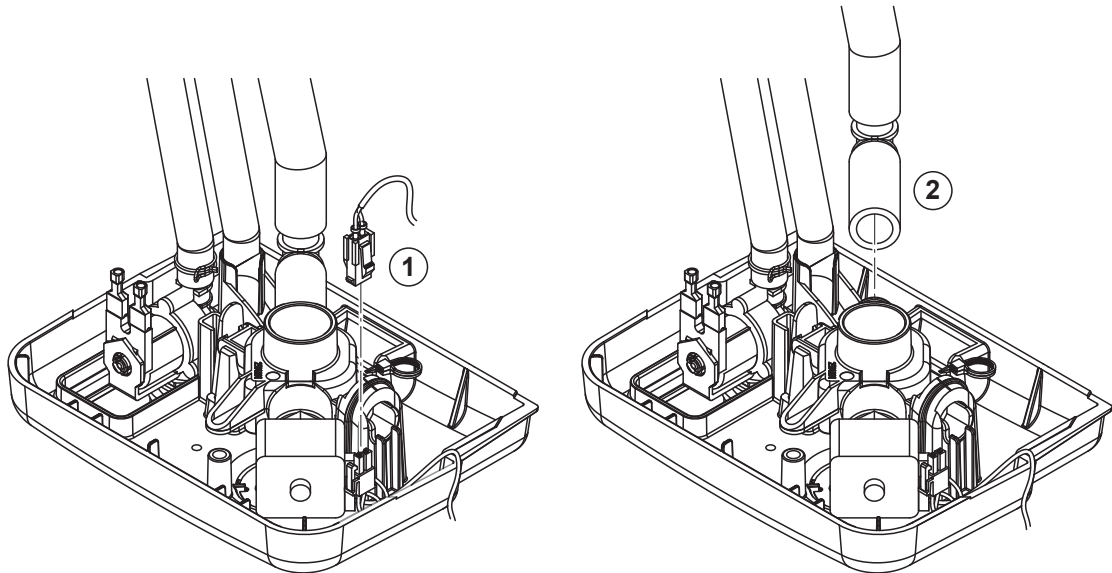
Anschlusskabel ausstecken und Schlauch abziehen
